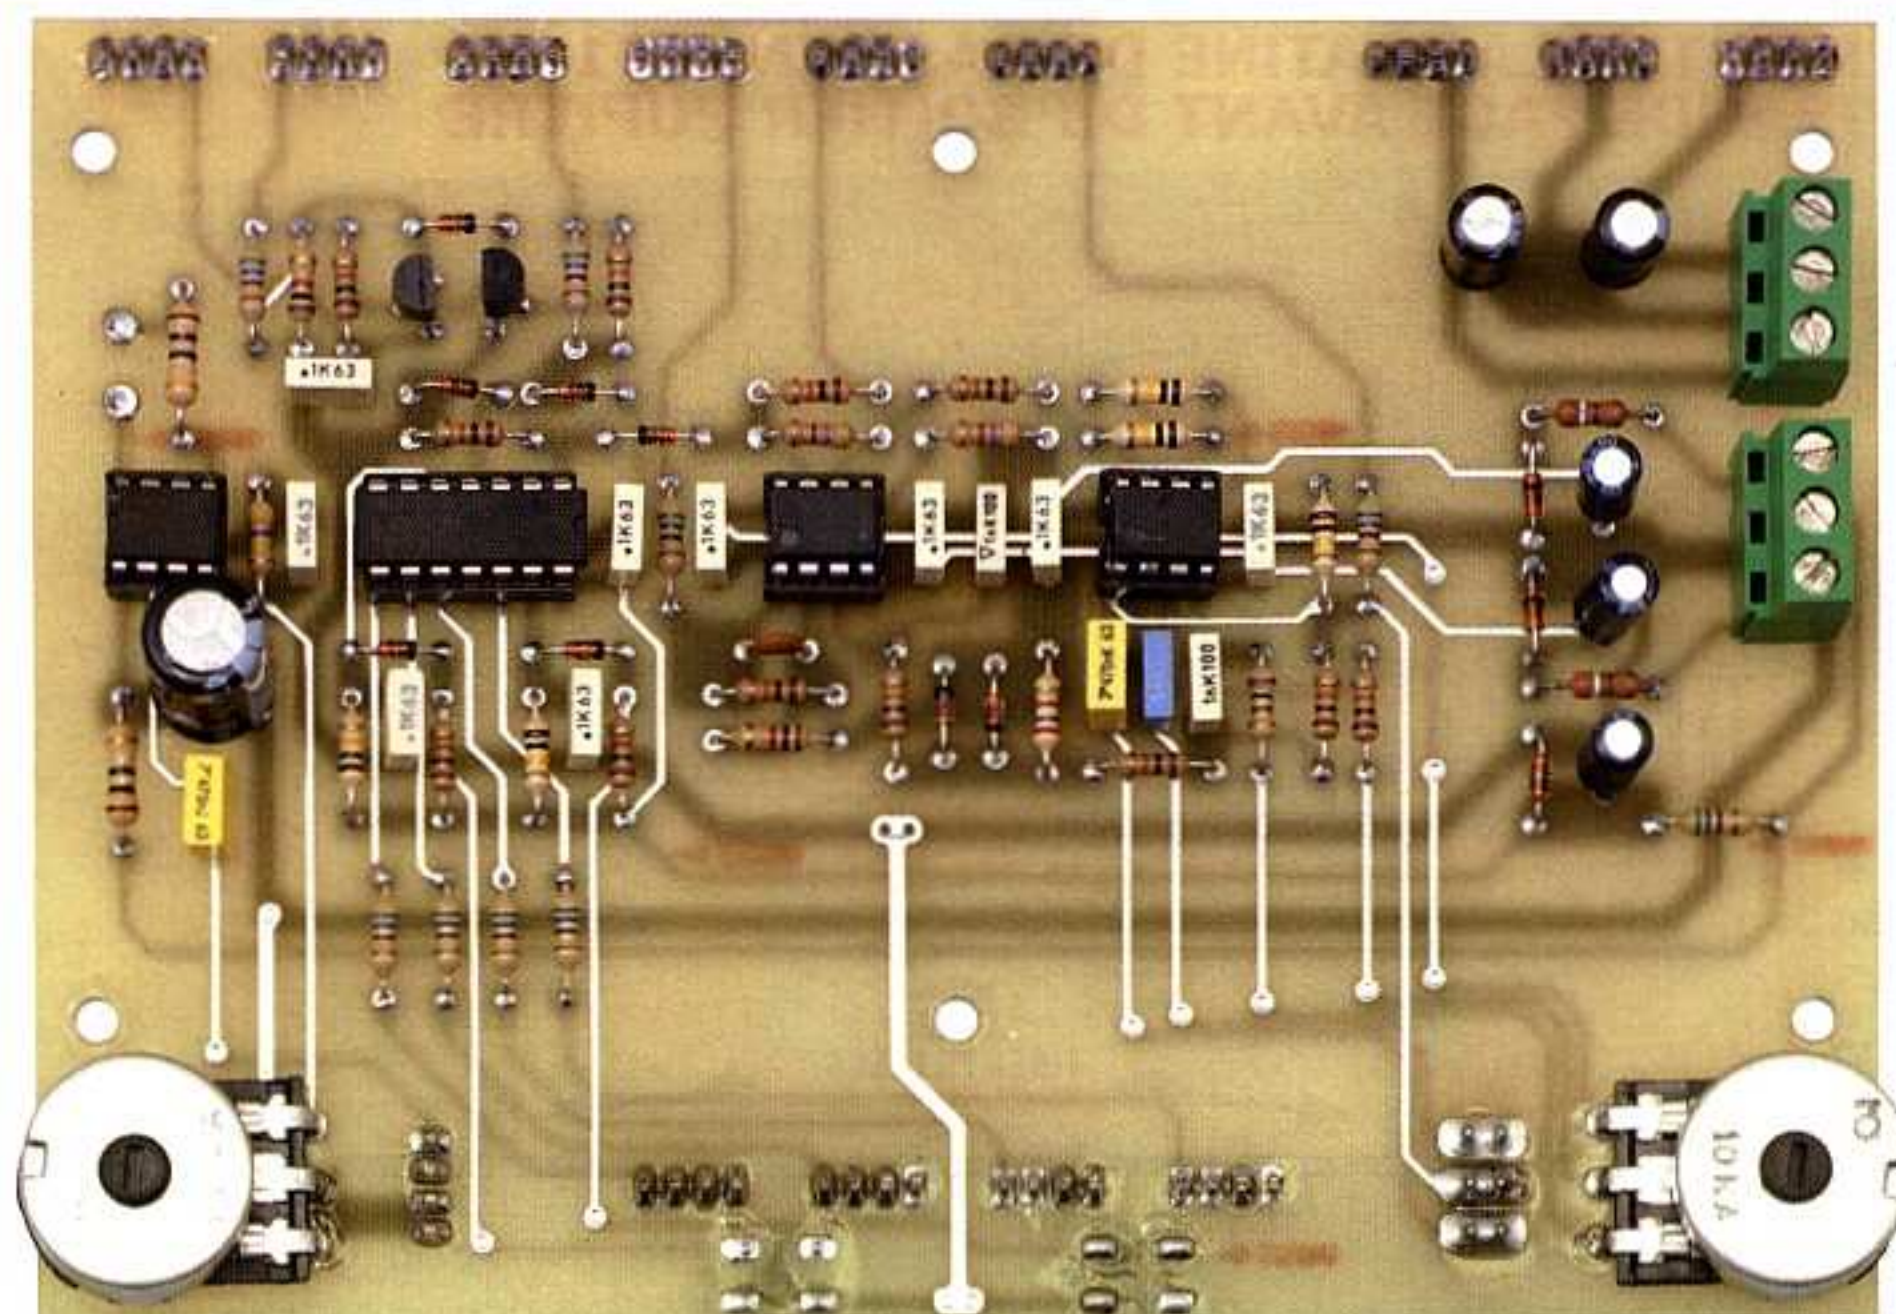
Photo d'un des prototypes de la platine de base EN3001 du MINILAB EN3000, côté composants.
